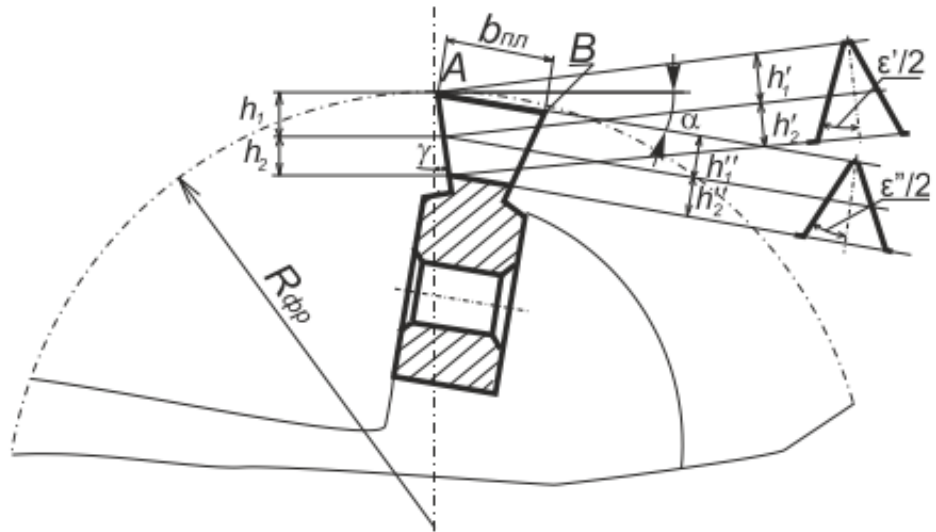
Схема встановлення твердосплавної непереточуваної пластинки у корпусі гребінчастої фрези
